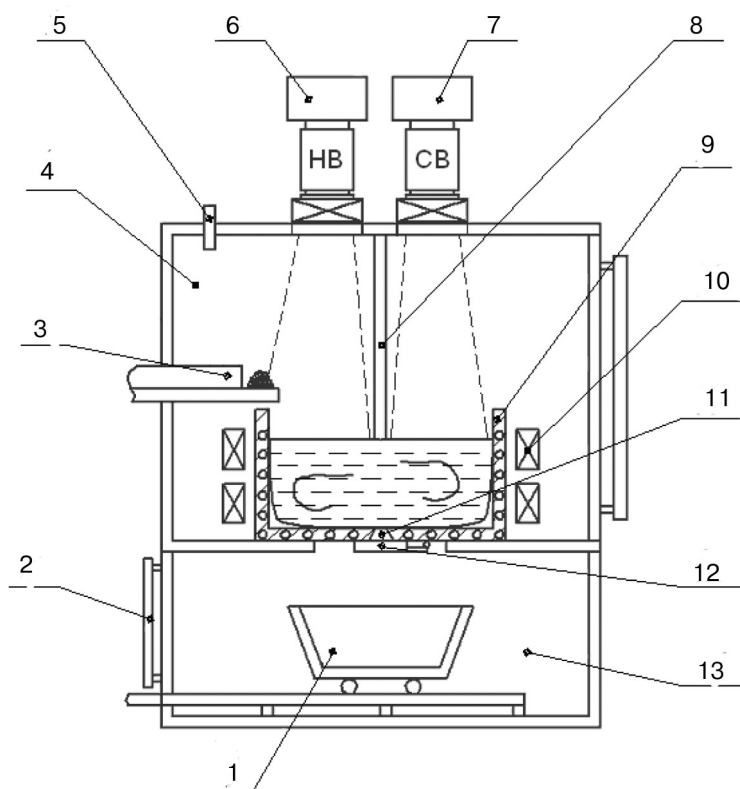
Схема установки для комбинированной обработки расплава в низком и среднем вакууме: 1 – литейная форма; 2 – крышка камеры литейных форм; 3 – устройство загрузки шихты; 4 – плавильная камера; 5 – устройство подачи рафинирующего газа в камеру; 6 – низковакуумная пушка ВТР; 7 – средневакуумная пушка ВТР; 8 – перегородка; 9 – гарнисажный тигель; 10 – катушка системы ЭМП тигля; 11 – сливное отверстие тигля; 12 – крышка сливного отверстия; 13 – камера литейных форм
